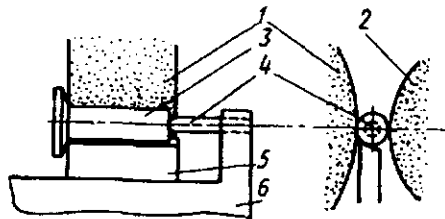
Схема расположения упора при бесцентровом врезном шлифовании: 1 – шлифовальный круг; 2 – ведущий круг; 3 – обрабатываемая деталь; 4 – упор; 5 – опорный нож; 6 – суппорт
